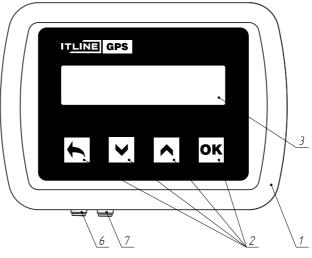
Внешний вид изделия сверху. Компактное базовое исполнение.
